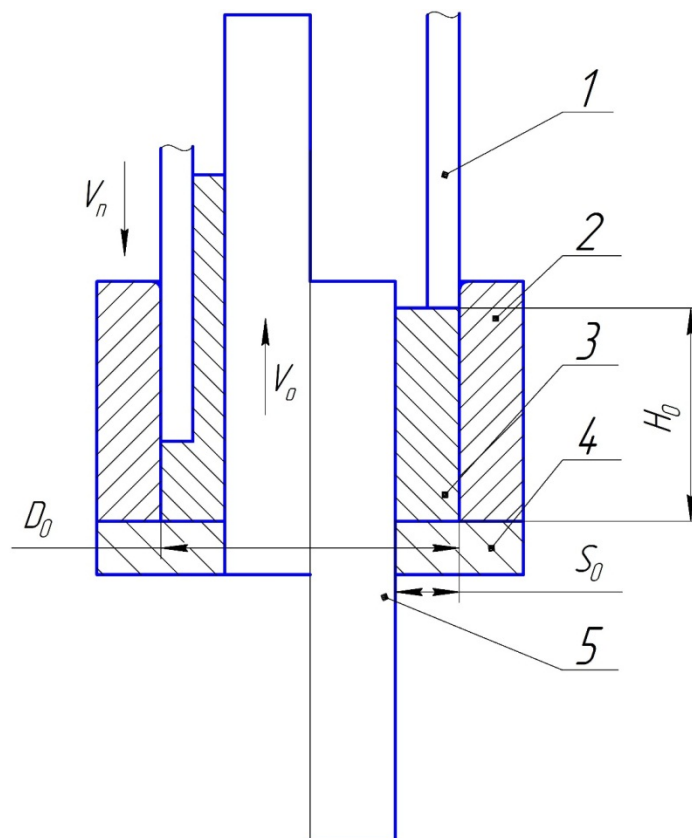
Схема процесу видавлювання фланців в штампах з активними силами тертя: 1 – пуансон, 2 – матриця, 4 – опора, 3 – заготовка, 5 – рухома оправка
